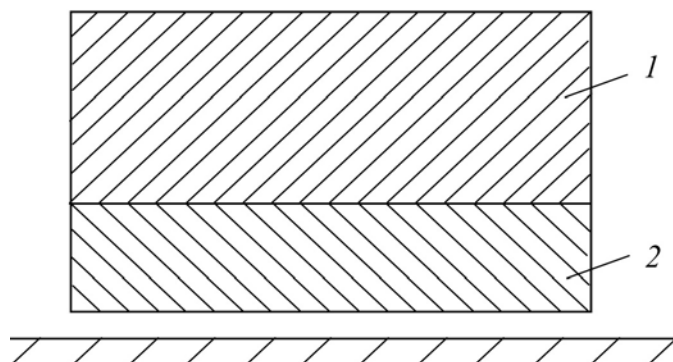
Конструкция подшипника скольжения со сплошной заливкой рабочей поверхности: 1 — сталь; 2 — оловянно-свинцовый сплав
